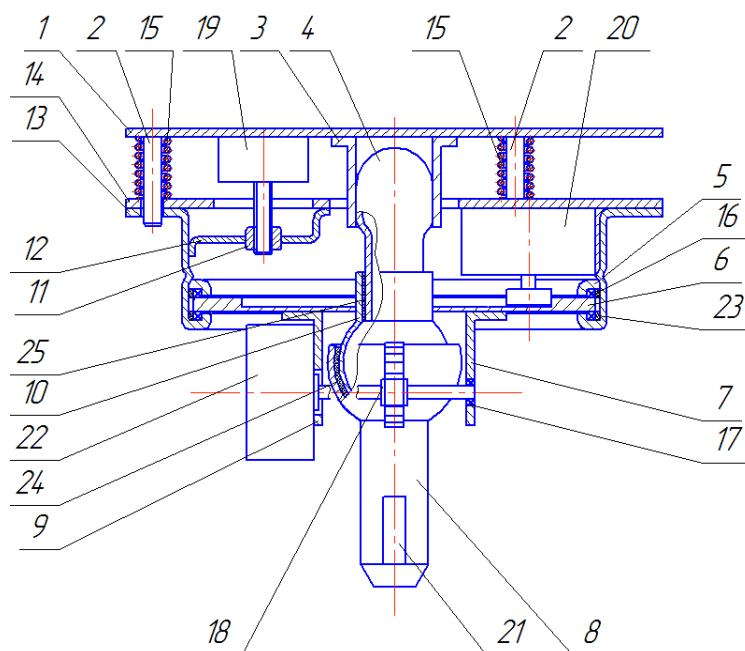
Конструкция модуля автоматического обнаружения и ликвидации очага возгорания: 1 – основание; 2 – ось; 3 – стакан; 4 – угольник; 5 – шайба; 6 – диск; 7 – опора; 8 – сопло; 9 – опора; 10 – втулка поворотная; 11 – втулка резьбовая; 12 – скоба; 13 – корпус; 14 – диск; 15 – пружина; 16 – шарик; 17 – подшипник; 18 – шестерня; 19 – электропривод постоянного тока; 20 – сервопривод; 21 – пирометрический датчик; 22 – сервопривод; 23–25 – уплотнения
